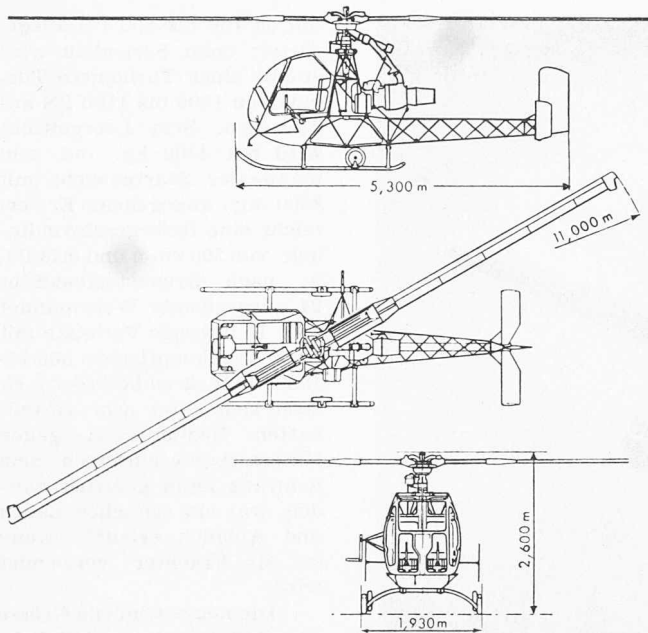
Der Düsenhubschrauber «Djinn SO 1221», 1:120
